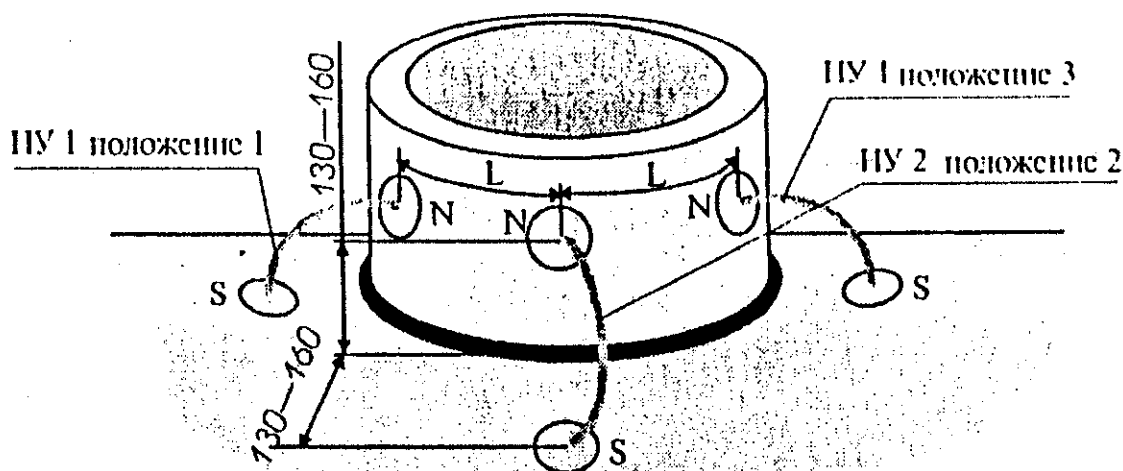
Контроль сварного шва соединения горловины люка с котлом
